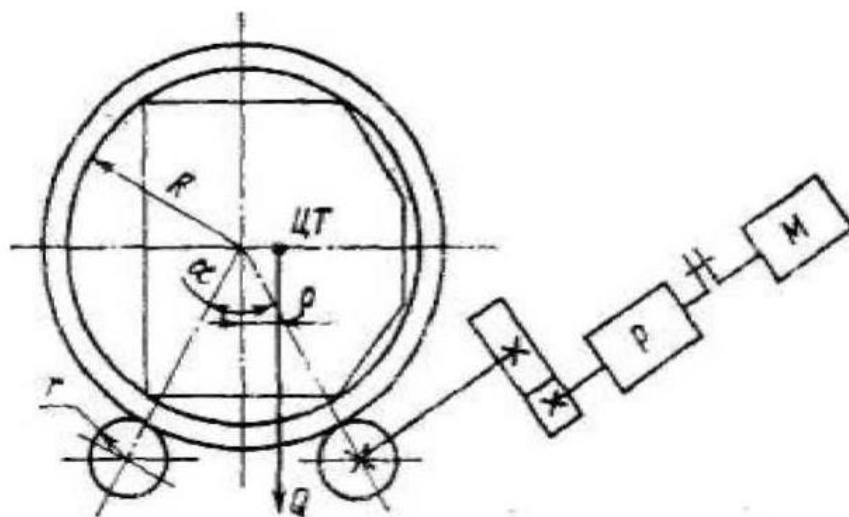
Расчётная схема роликового стенда с жёсткой кинематической связью:
